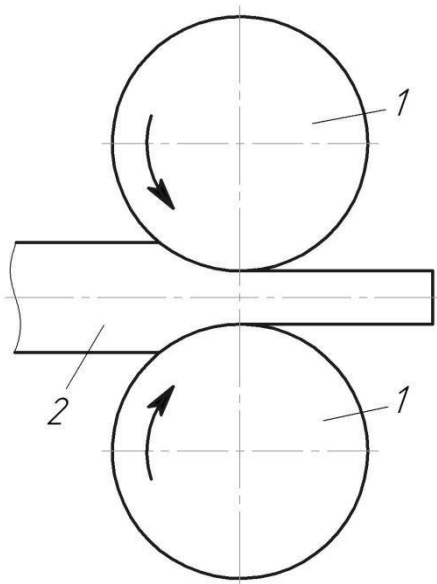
Схема поздовжнього прокатування: 1 – прокатні валки; 2 – смуга, що обробляється
